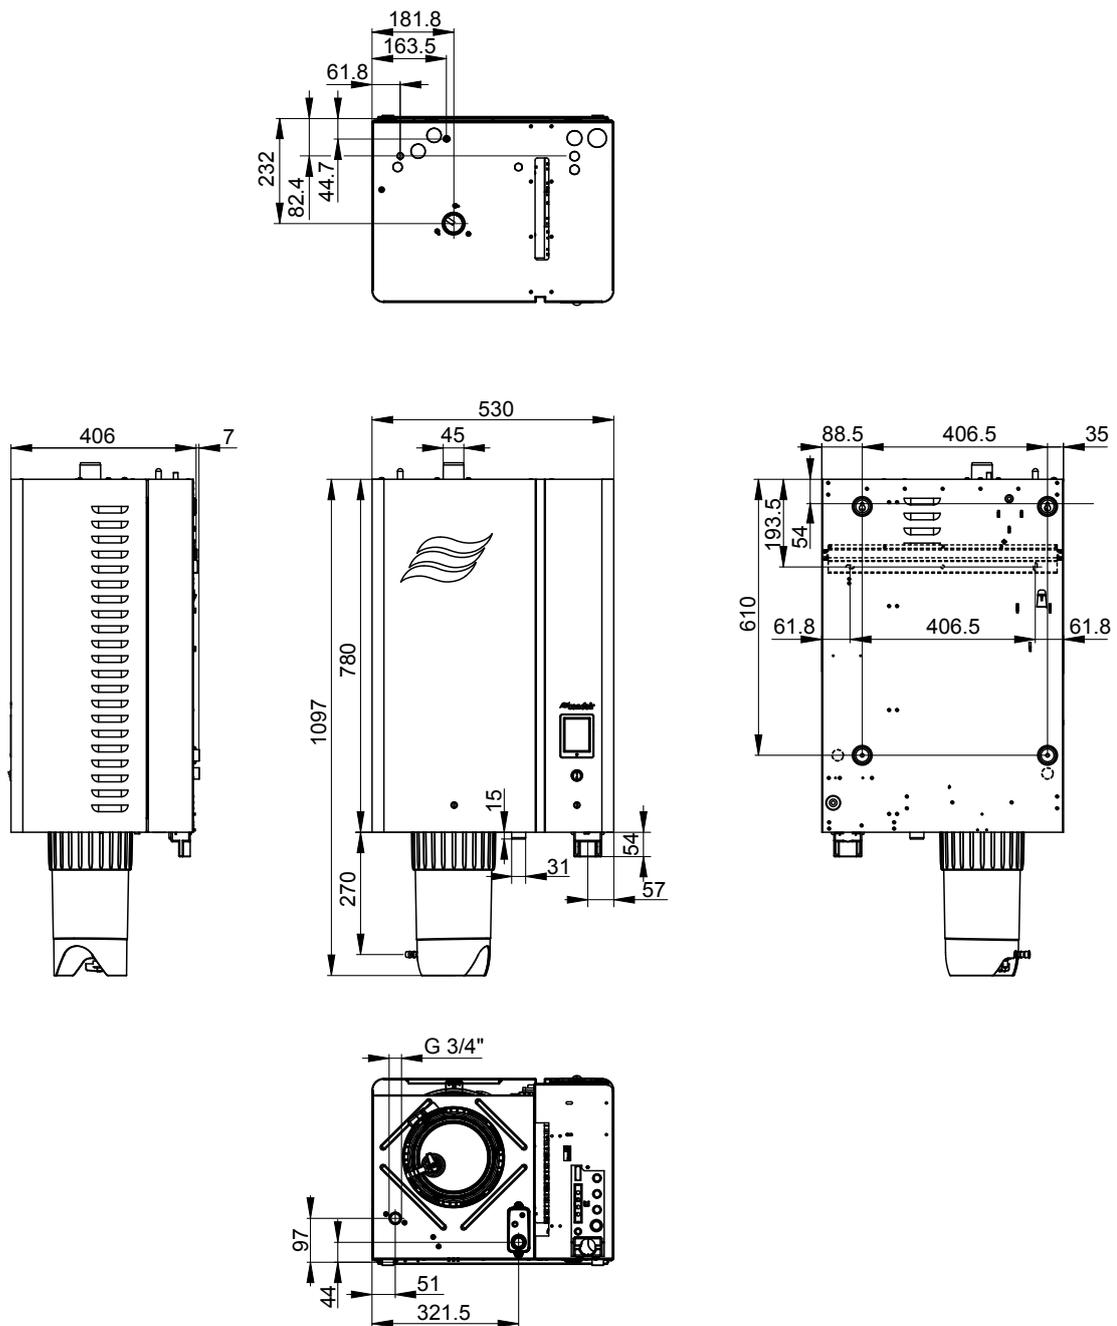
Dimensioni del modulo "M" (misure in mm)
